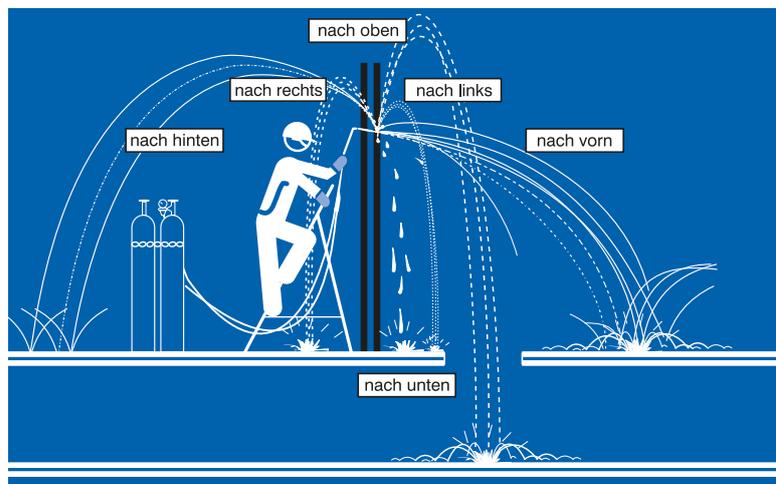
Ausbreitungsverhalten heißer Partikel bei schweißtechnischen Arbeiten
